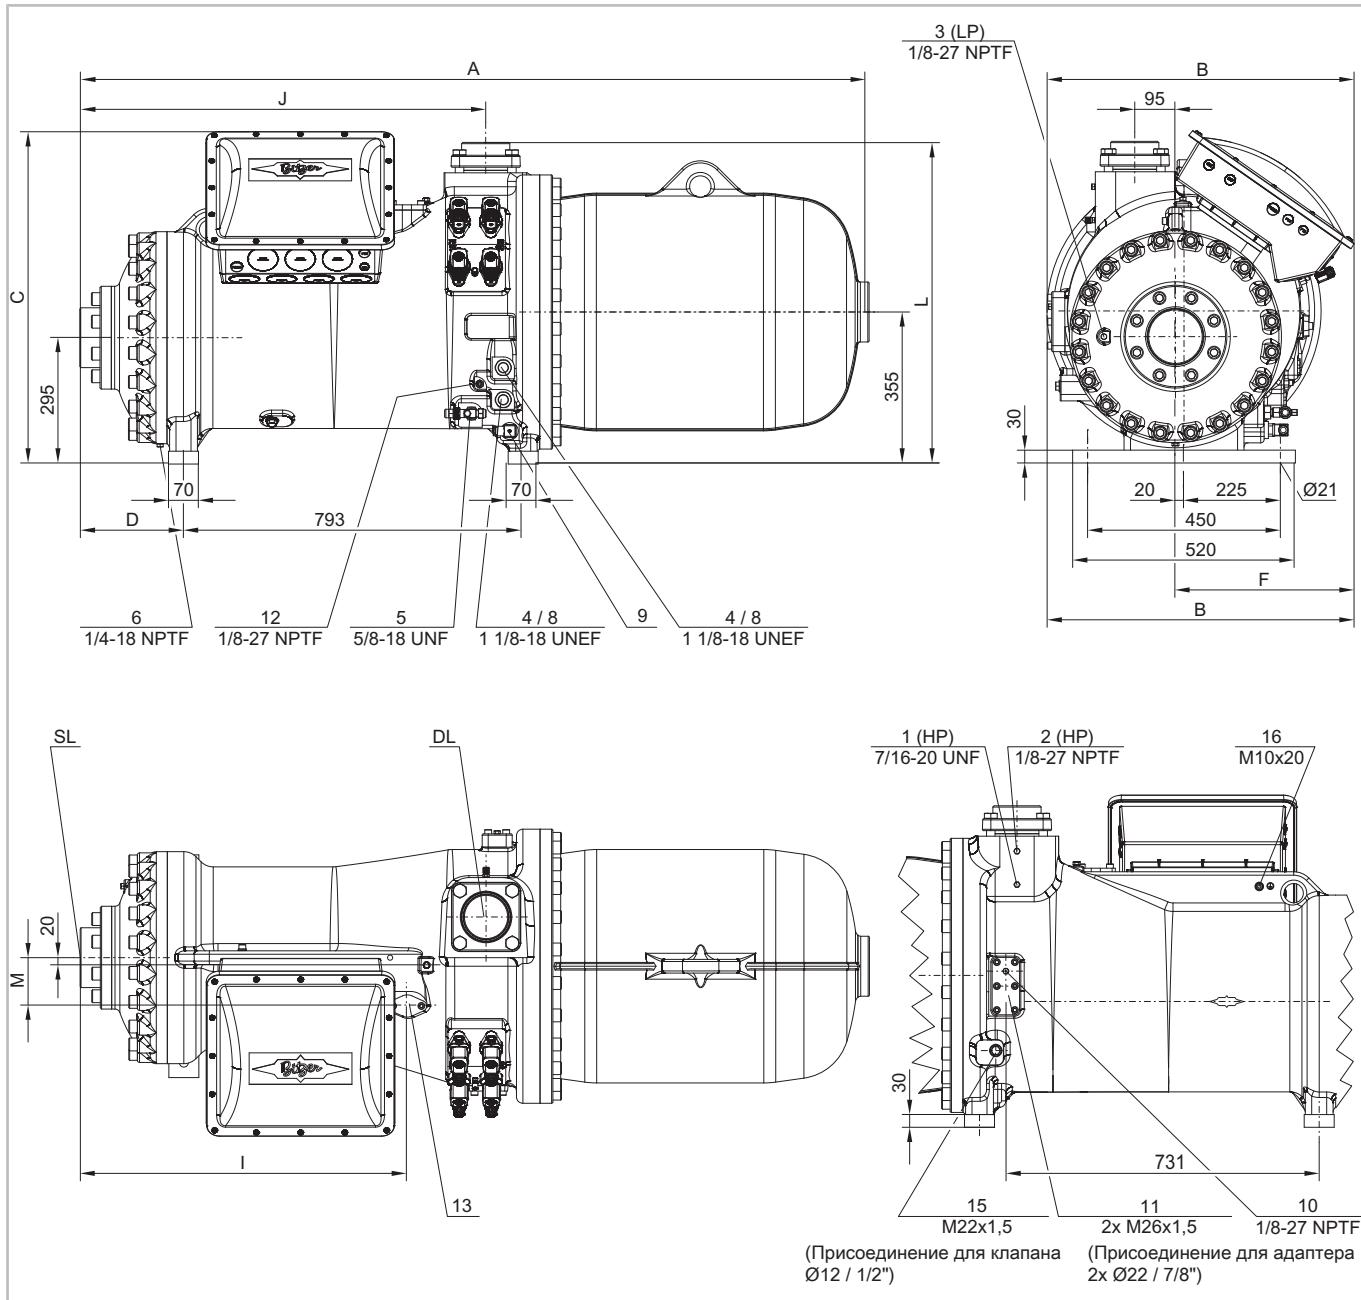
Чертежи с указанием размеров для CSH9553-180(Y) .. CSH95113-320Y
